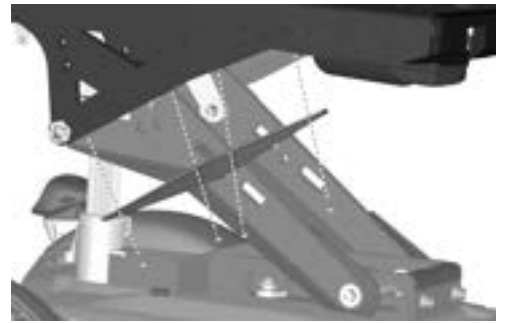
Der Einklemmschutz ist mit vier Schrauben montiert.
